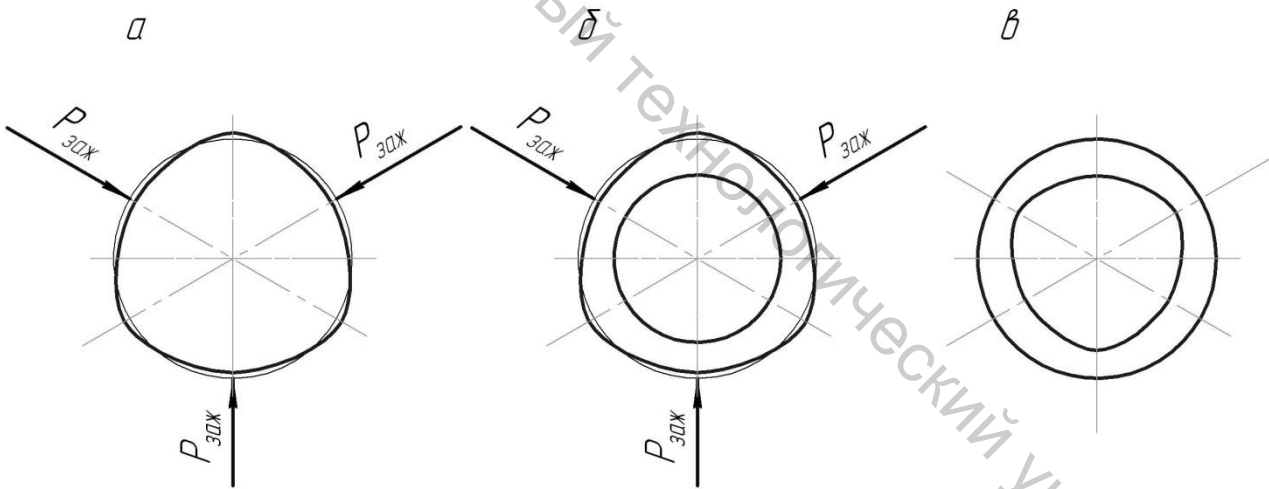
Схема формирования погрешности формы при действии зажимающих сил: а – форма заготовки после закрепления; б – форма расточенного отверстия в закрепленной заготовке; в – форма отверстия после раскрепления заготовки
